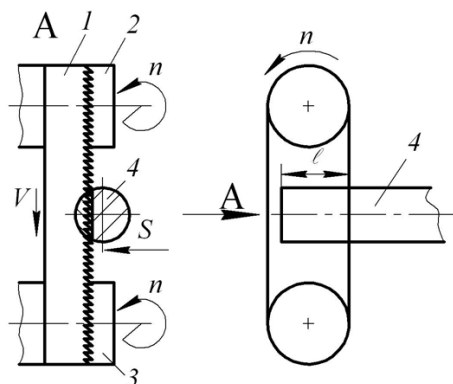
Схема отрезки заготовок на ленточно-отрезном станке:
